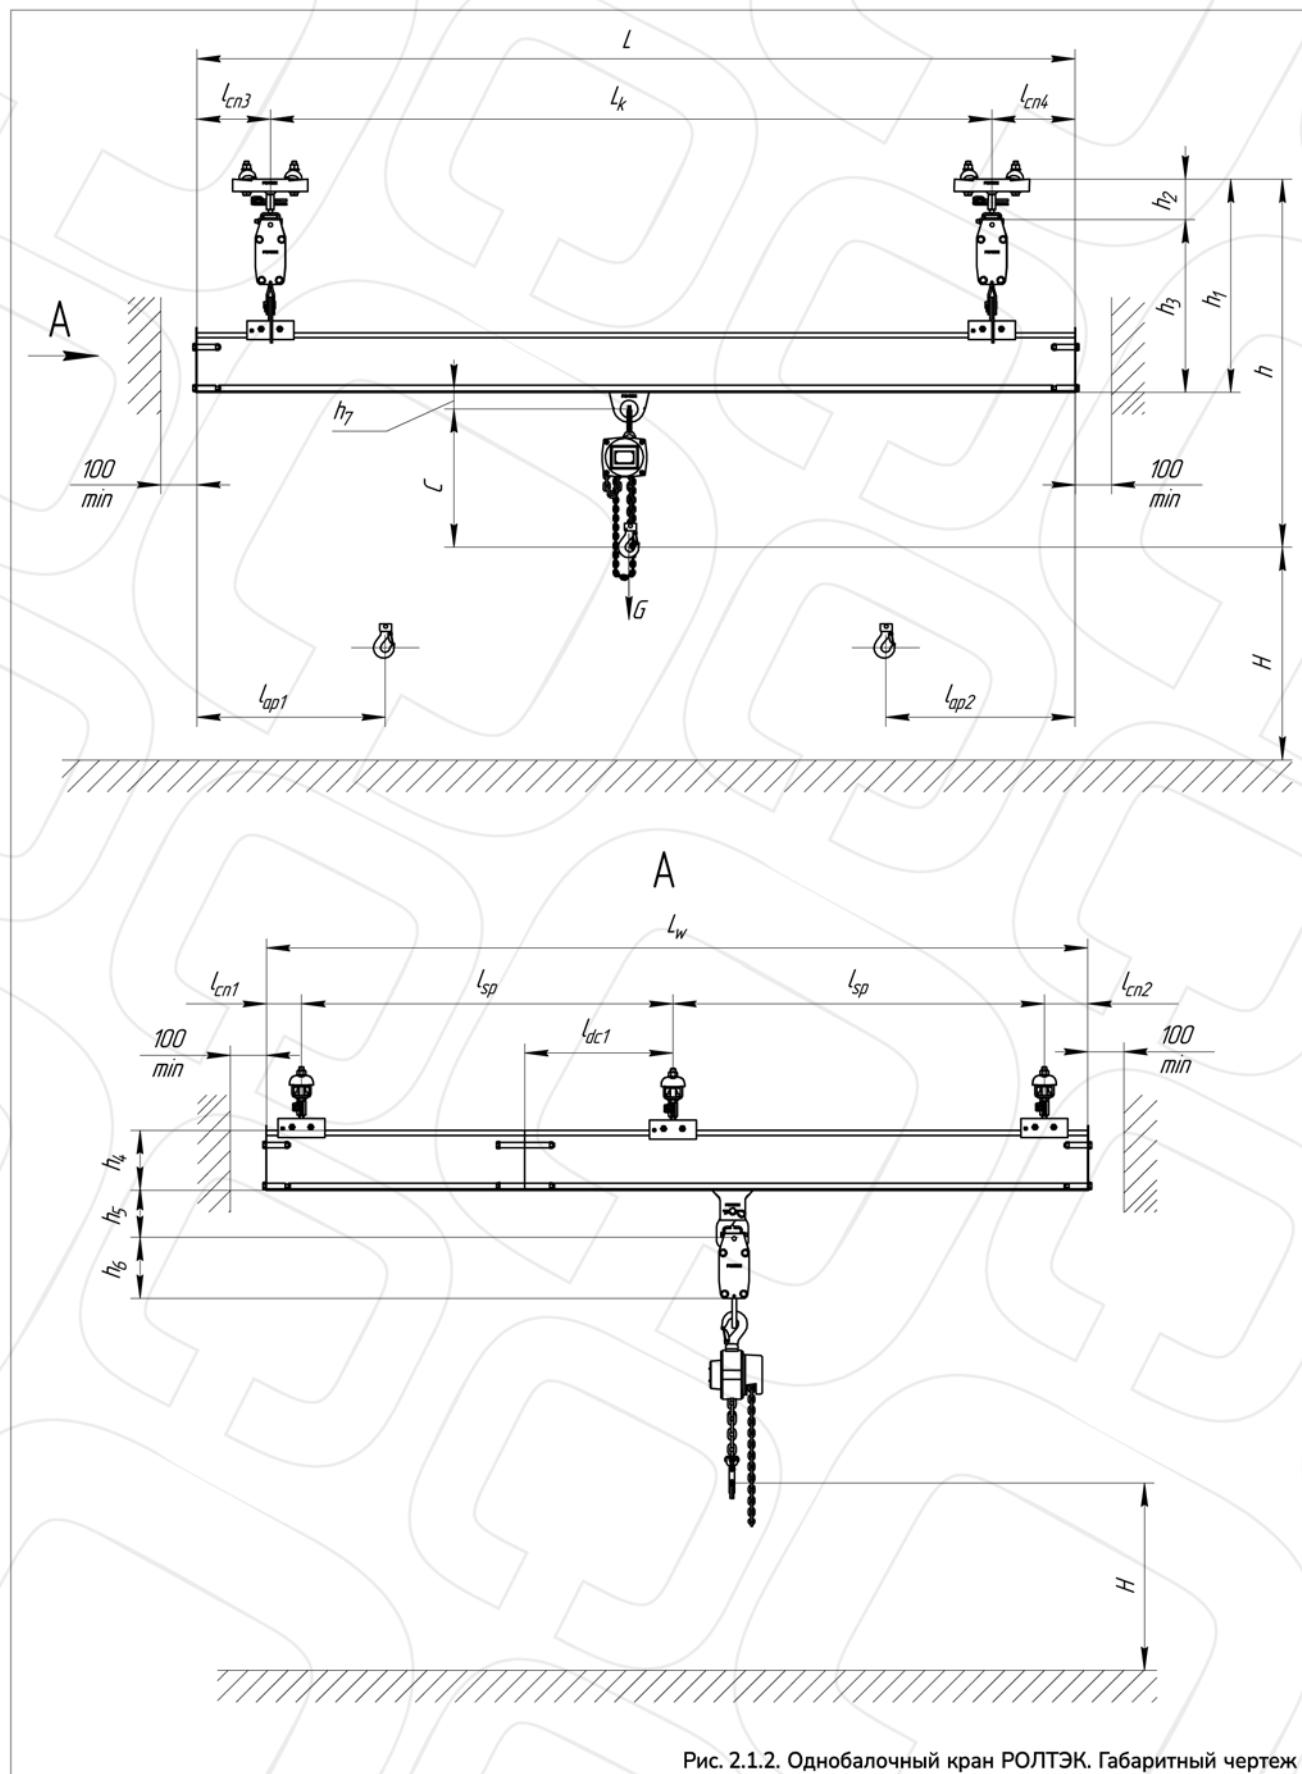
Однобалочный кран РОЛТЭК. Габаритный чертеж
